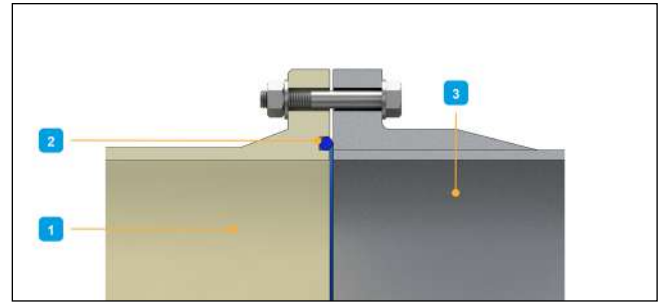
Flange fixa em PRFV utilizando uma junta tórica
